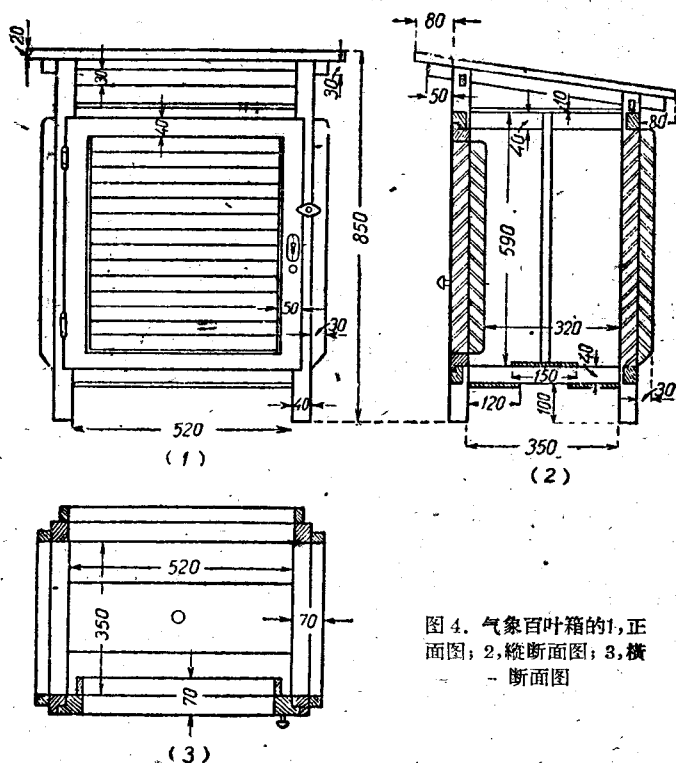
气象百叶箱的1, 正面图; 2, 纵断面图; 3, 横断面图
